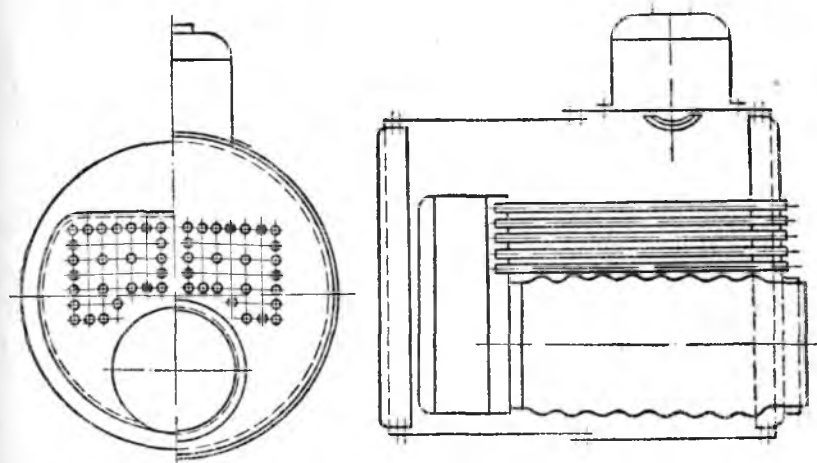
Цилиндрический оборотный котел с полуприставной топкой.
